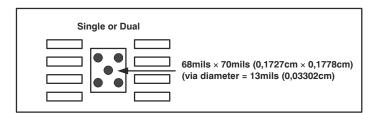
PowerPAD Integrated Circuit Package PCB Etch and Via Pattern
